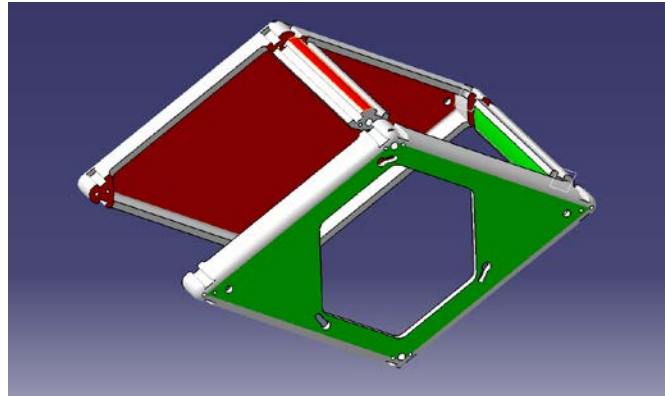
Subdivisión de piezas para la impresión. Las caras de apoyo se muestran en verde.
